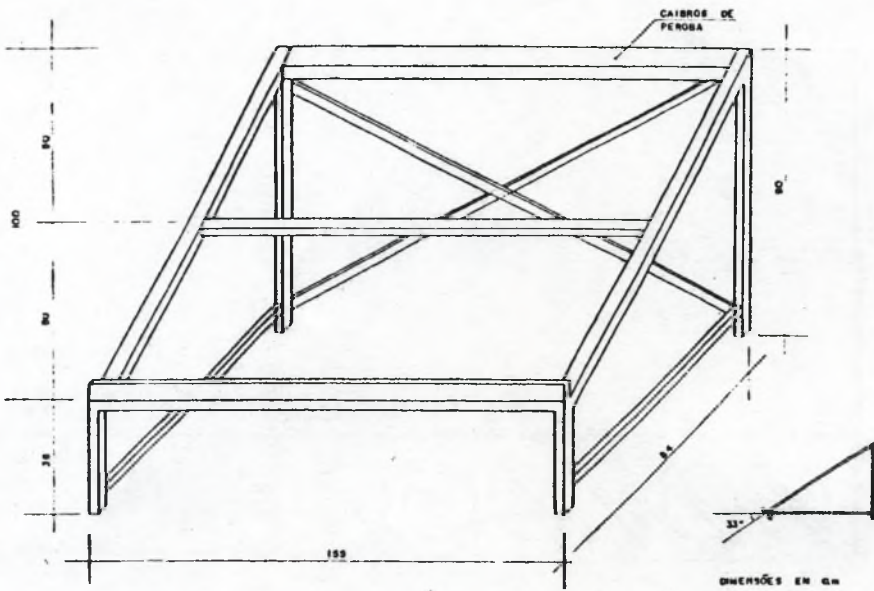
(continuação). Projeto para construção do coletor solar (dimensões em cm).
